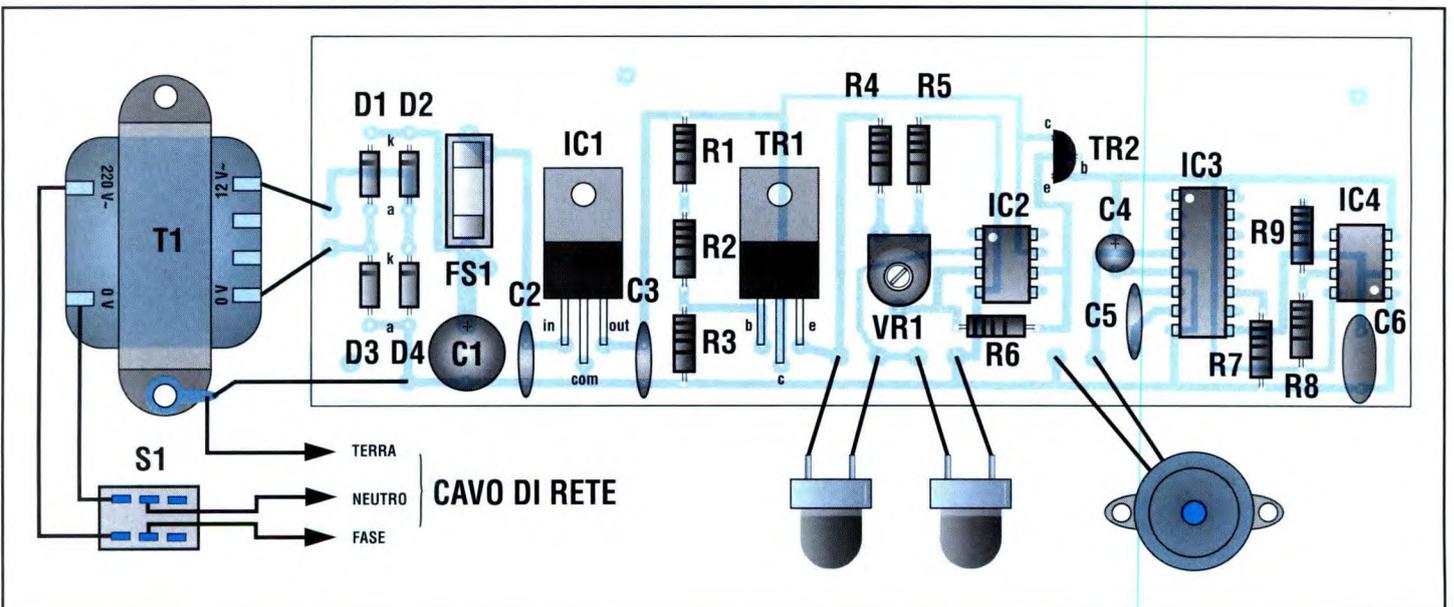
Disposizione dei componenti sulla bassetta stampata.
